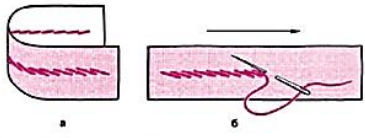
Стельчатые стежки: а — вид с лицевой стороны и с изнаночной стороны; б — выполнение стежков
